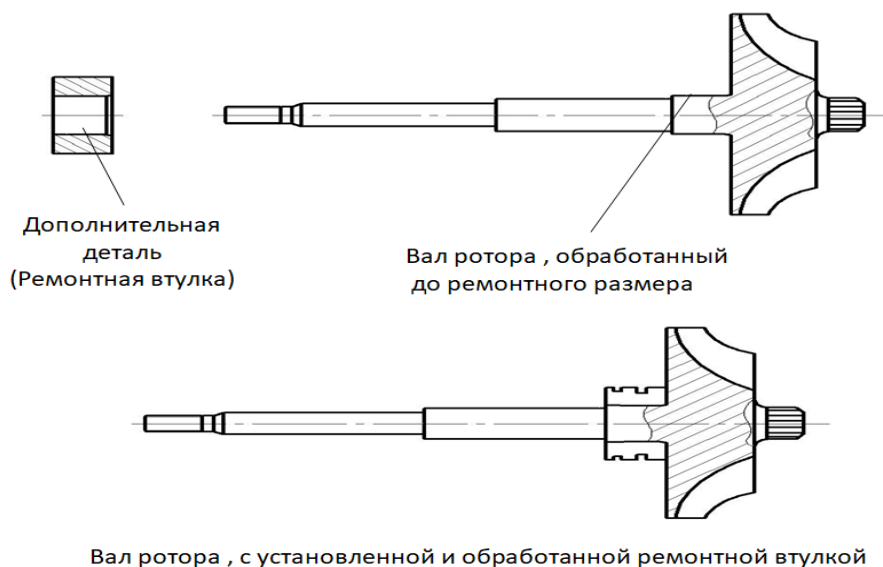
Метод установки дополнительной детали применительно к валу ротора турбокомпрессора
